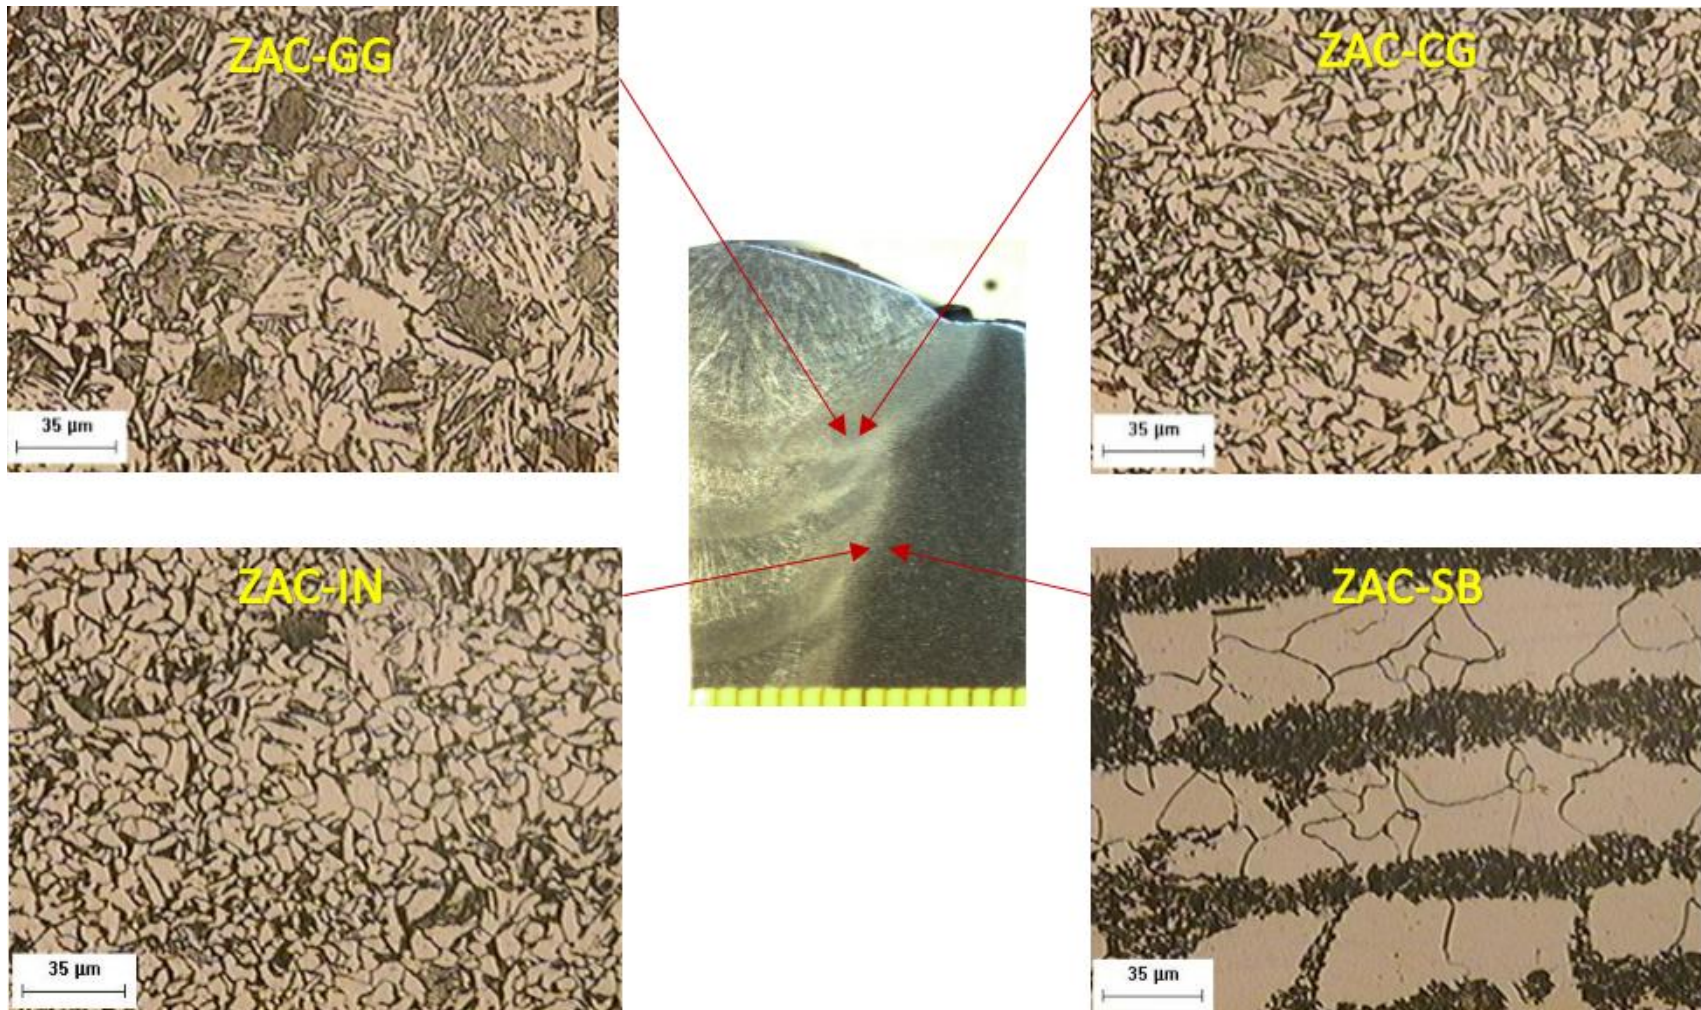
Regiones en la ZAC. Proceso de soldadura FCAW, H.I. = 3.5 KJ/mm.
